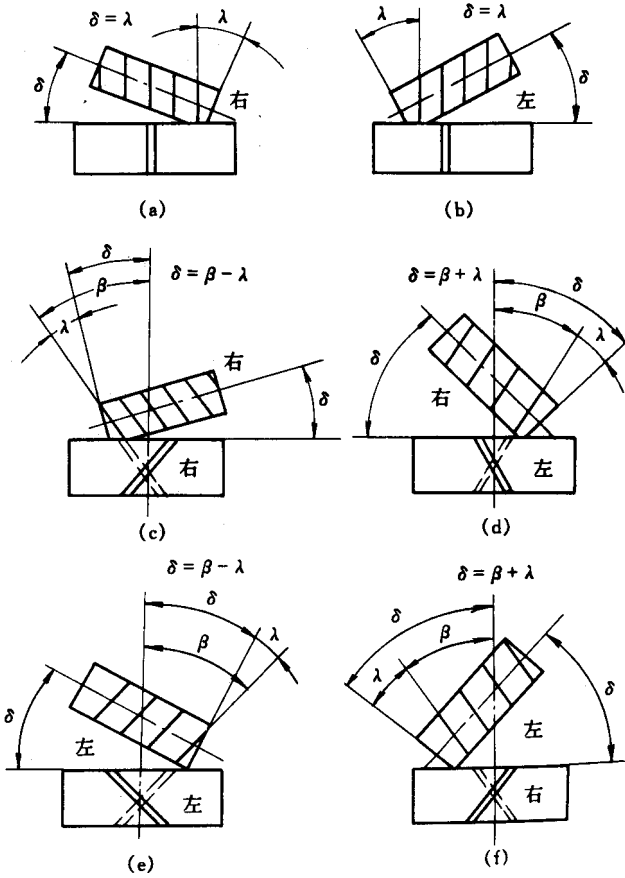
加工斜齿圆柱齿轮时滚刀的安装角度
